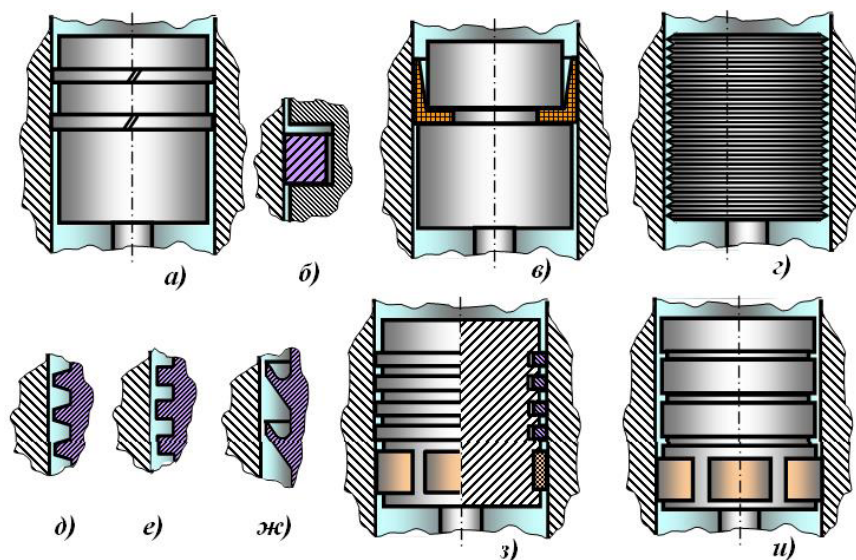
Конструкции уплотнений в цилиндропоршневых группах компрессоров:
